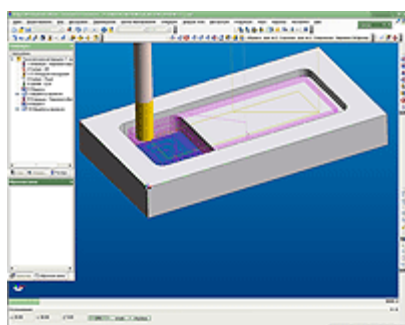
Edgescam. После выбора заготовки перейти в режим обработки и обработать детали.
